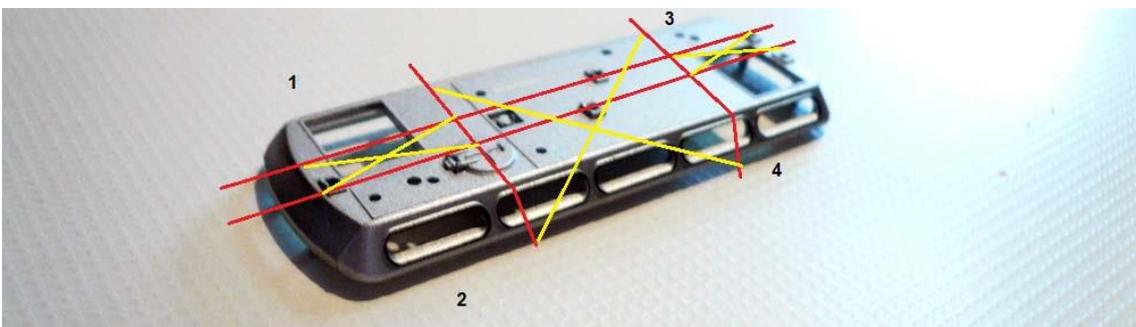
Pieza para modificar y construir la cabina observatorio.
